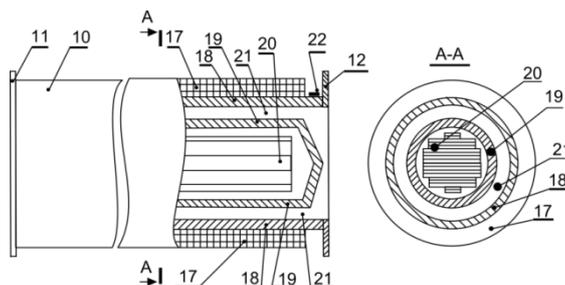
а) Конструкция фазы нагревательного устройства с частичным разрезом, б) Разрез фазы нагревательного устройства по А-А на рисунке 10
